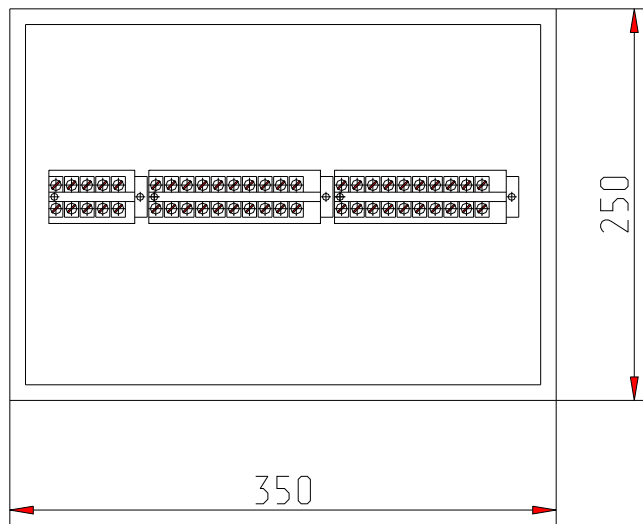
Внешний вид коробки клеммной типа КК - 25 УХЛ4.
